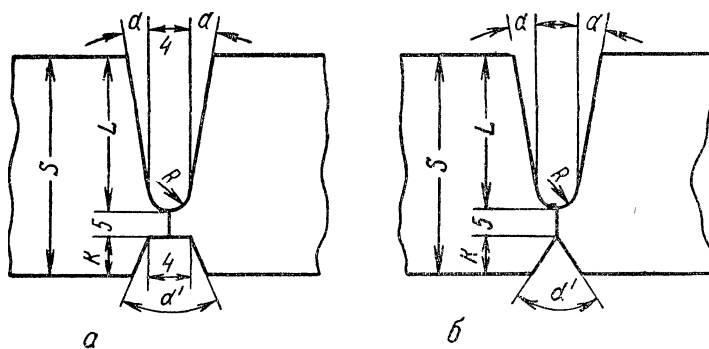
Разделка кромок для односторонней многопроходной сварки
